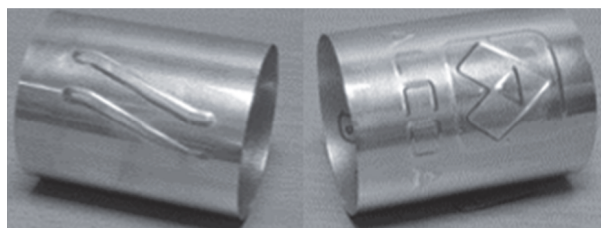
Примеры деталей с рельефом на боковой поверхности
